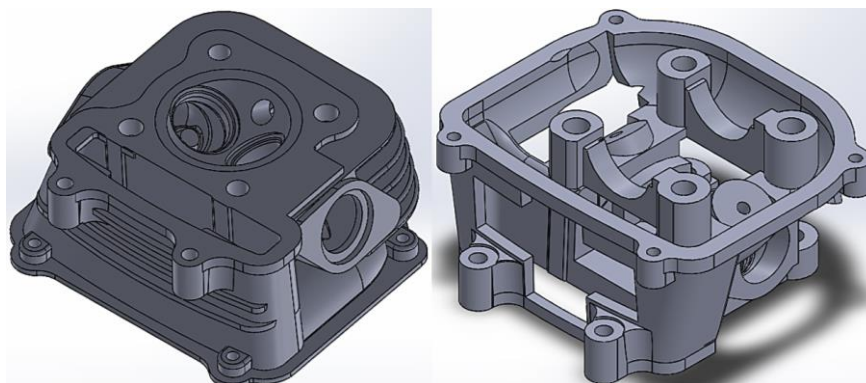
Impresión 3D para comprobación de geometría a fabricar.
